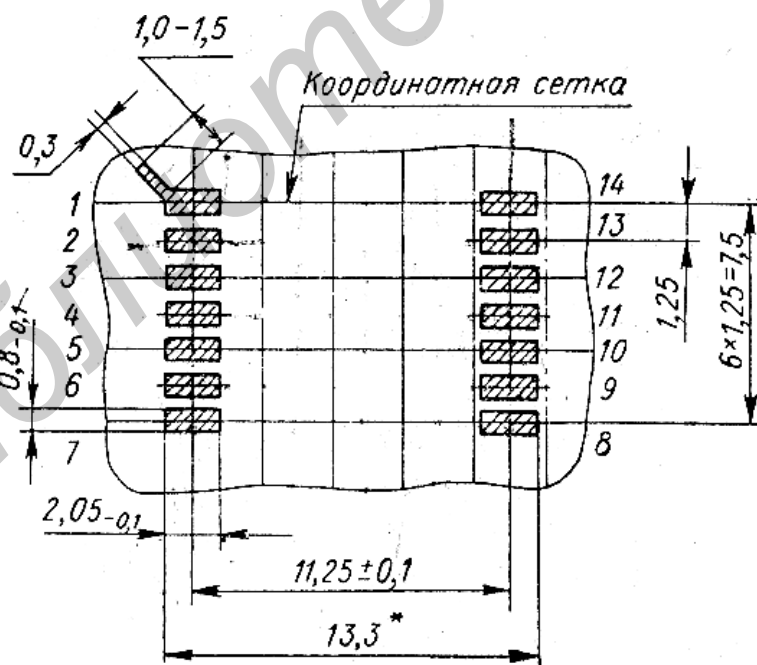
Разметка посадочного места для микросхем в корпусах типа 4 с прямоугольными контактными площадками:
